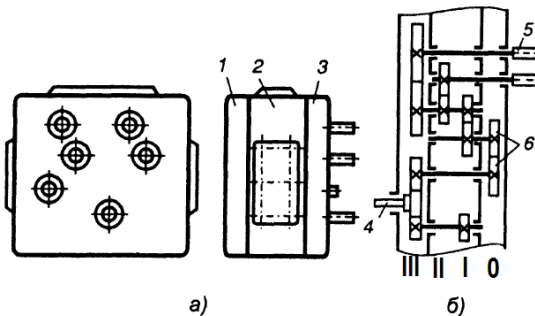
Шпиндельна коробка агрегатного верстата
